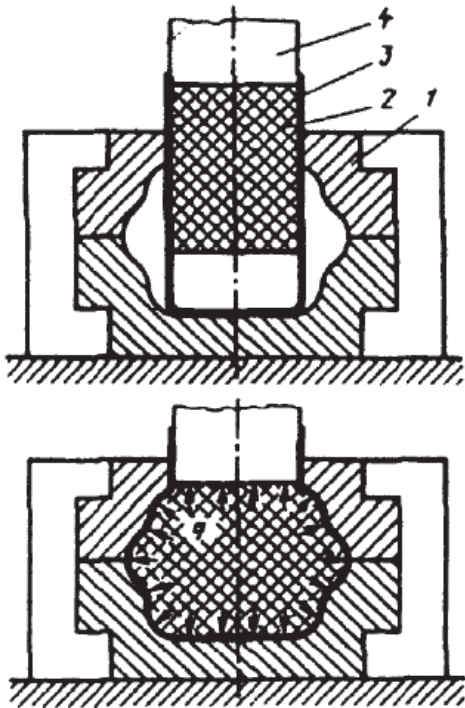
Схема штампа для формування просторової деталі [3]:
